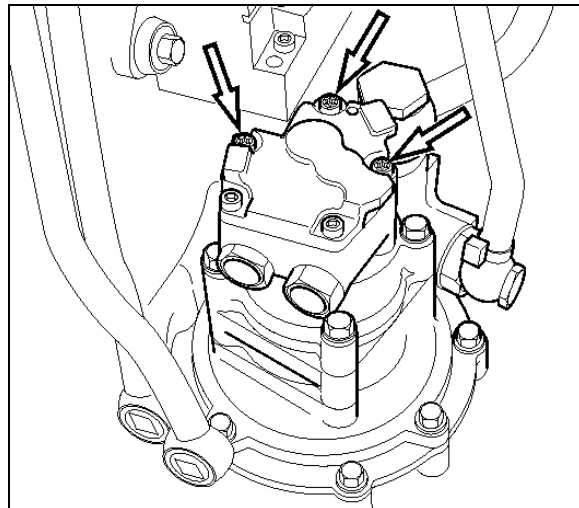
DÉPOSE DE LA POMPE À CARBURANT
